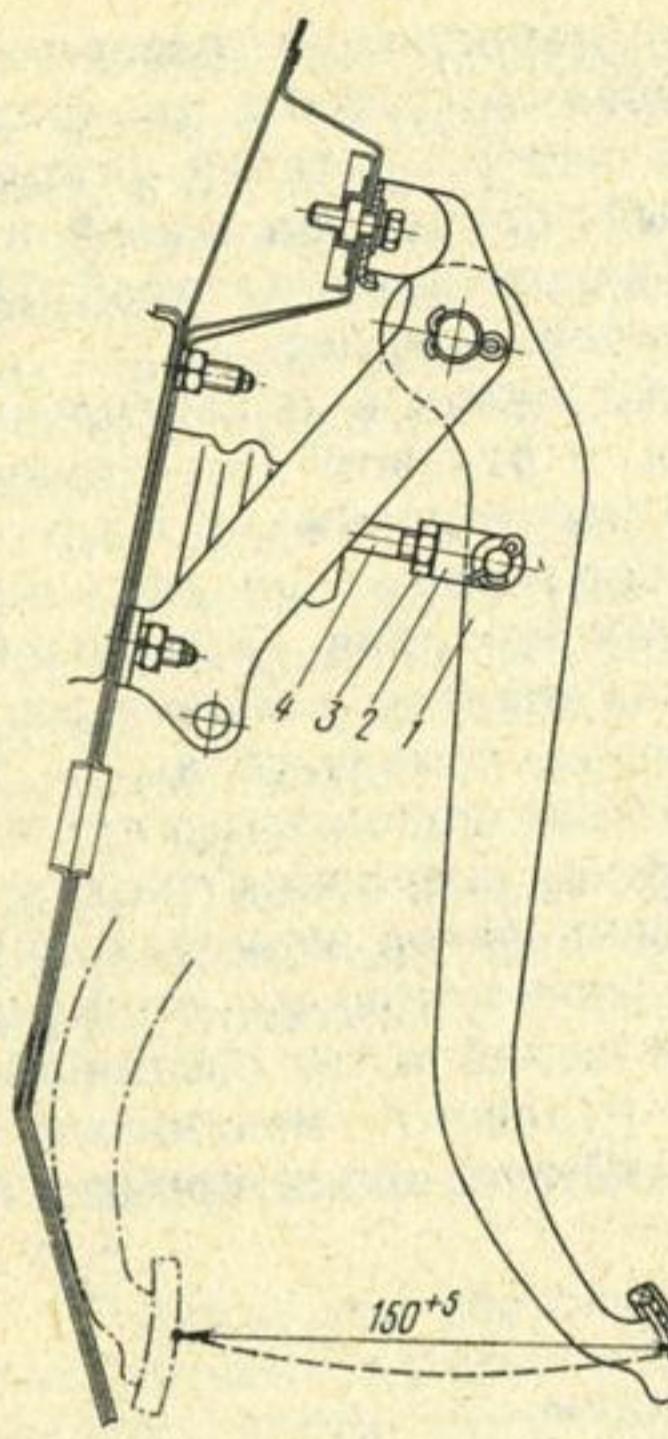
Регулировочный узел положения педалей сцепления и тормозной
